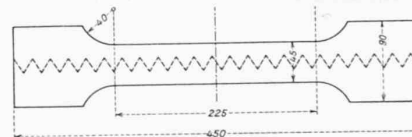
Zerreißprobestab mit Schweissnaht in der Stabaxe.
